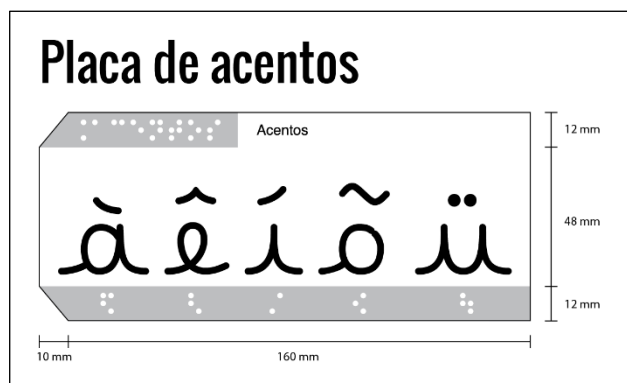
Desenho técnico da placa de acentos (fonte: a autora)
